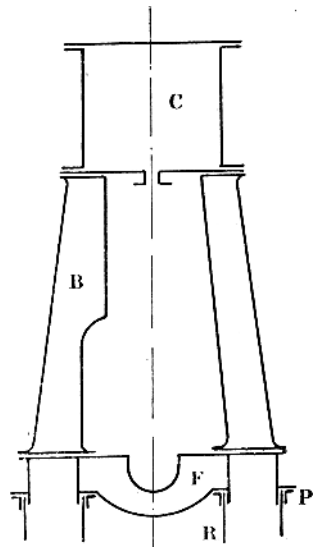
Cylindre avec bâtis, plaque de fondation, plan de pose
